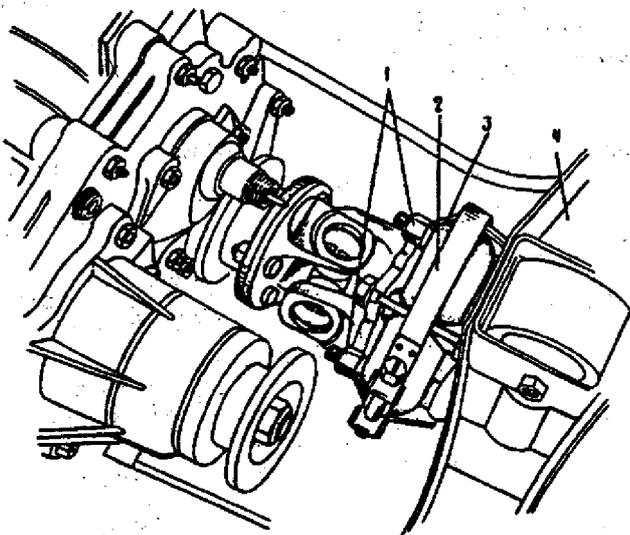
Acoplamento elástico de união da árvore longitudinal com a caixa de mudanças: 1 - porcas de fixação do flange do cardã ao acoplamento elástico; 2 - braçadeira A.70025; 3 - acoplamento elástico; 4 - travessa do suporte traseiro do motor.
